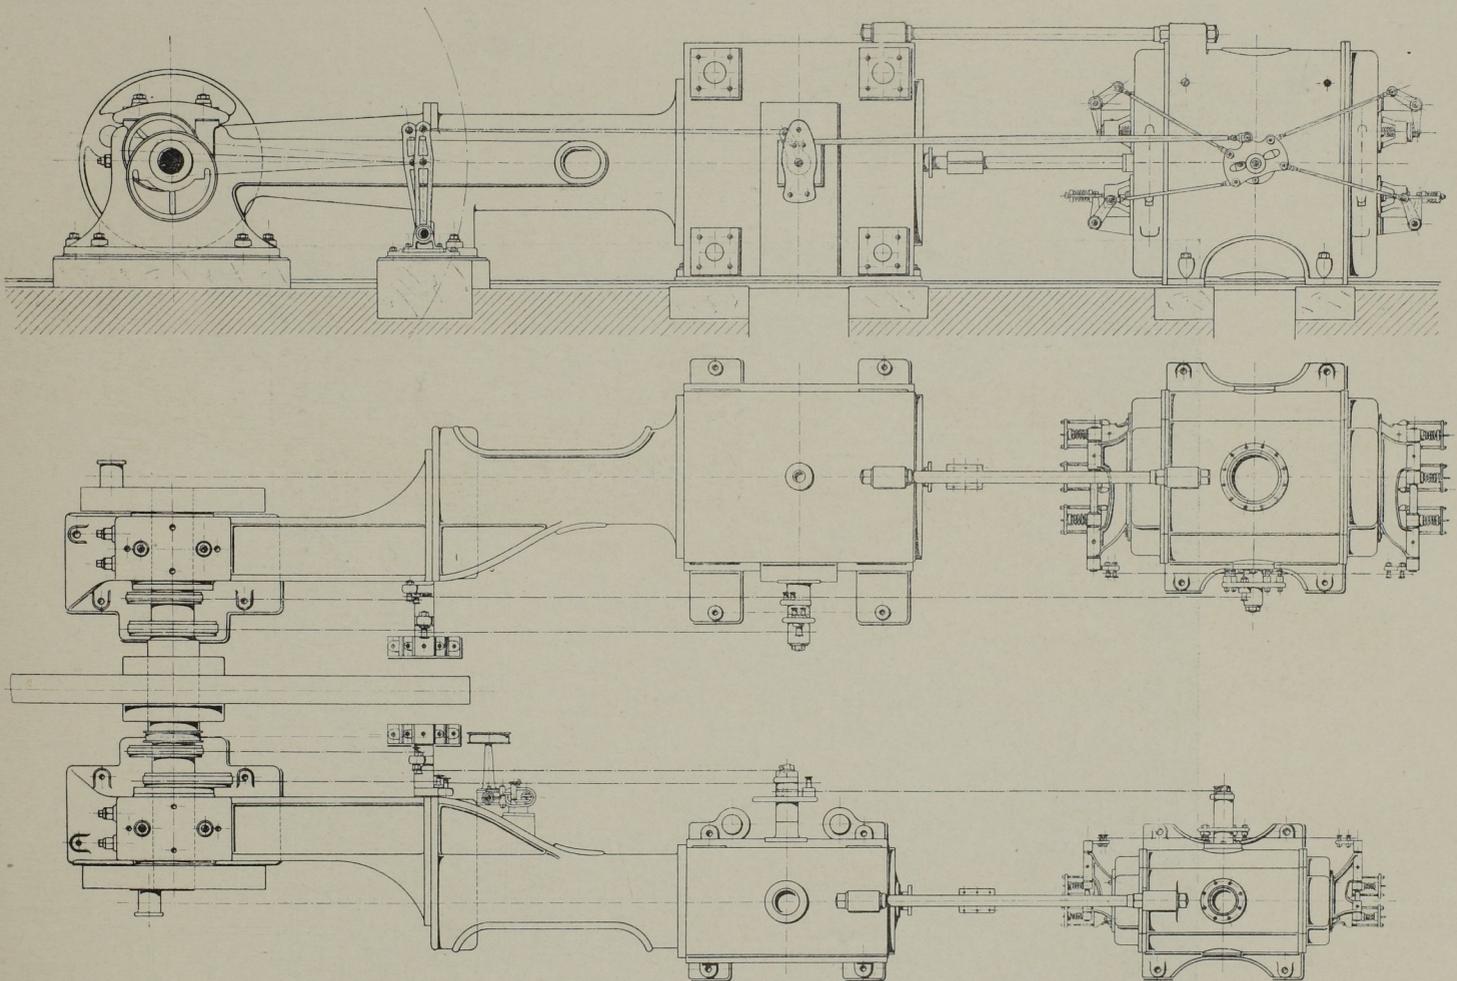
Grundriss. Massst. 1 : 64.
